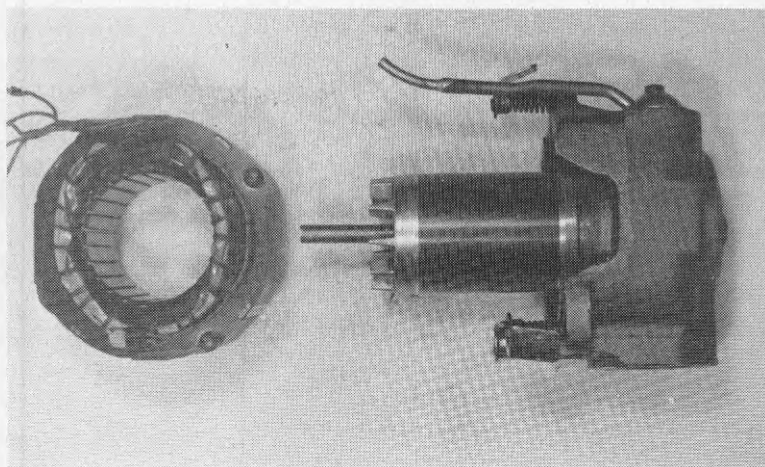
Vevaxel och rotor till kompressor nr 1.
